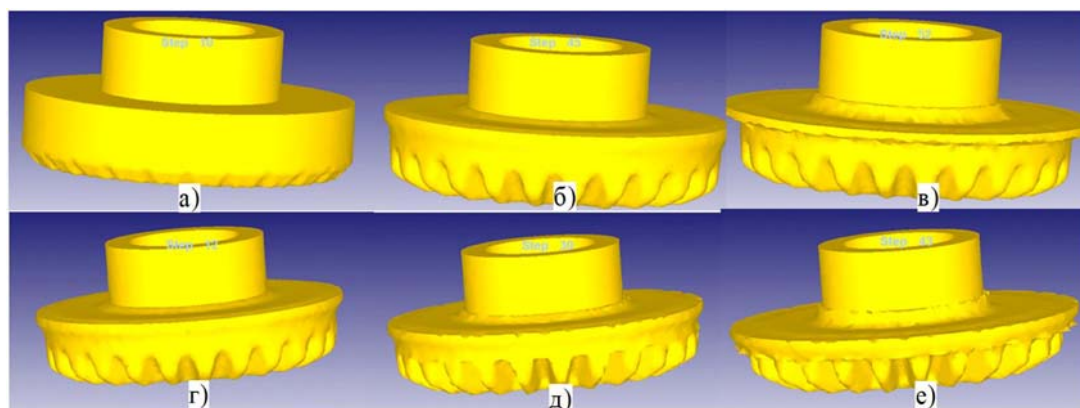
Модель штамповки конического зубчатого колеса по стадиям штамповки: 1 переход (а, б, в); 2 переход (г, д, е)
